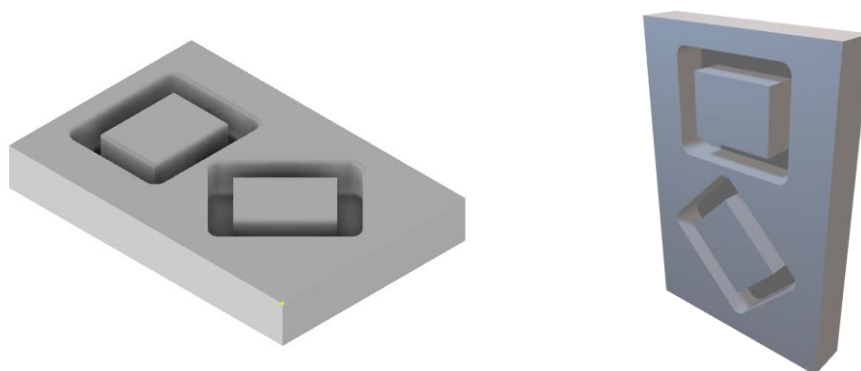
Τρισδιάστατη απεικόνιση αποστολής 49
